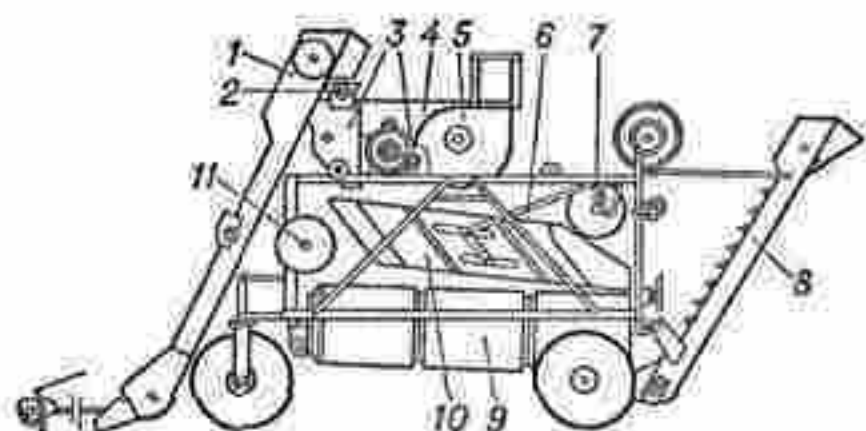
Зерноочистительная машина ОС-4,5А: 1 — загрузочный транспортер; 2 — питающий вал; 3 — приёмная камера; 4 — воздуховод; 5 — вентилятор; 6 — шатун; 7 — приводной вал; 8 — отгрузочный транспортер; 9 — триер; 10 — решётный стан; 11 — эксцентриковый вал.
